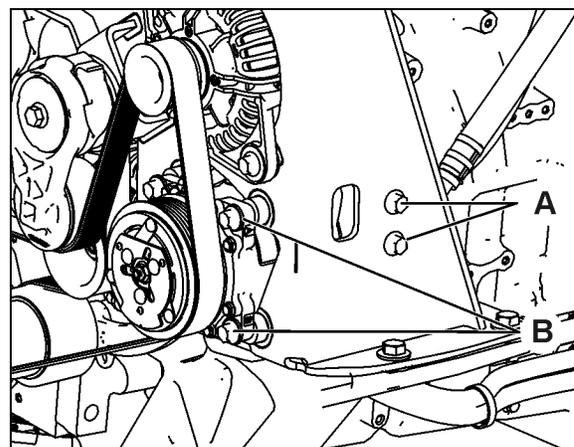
MONTAJE DE COMPRESOR SERIE X
